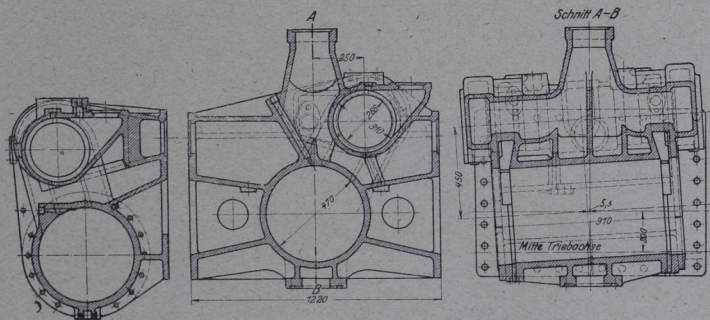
Innenzylinder der 2C-Drilling-H.S.L., dänische Staatsbahn.
